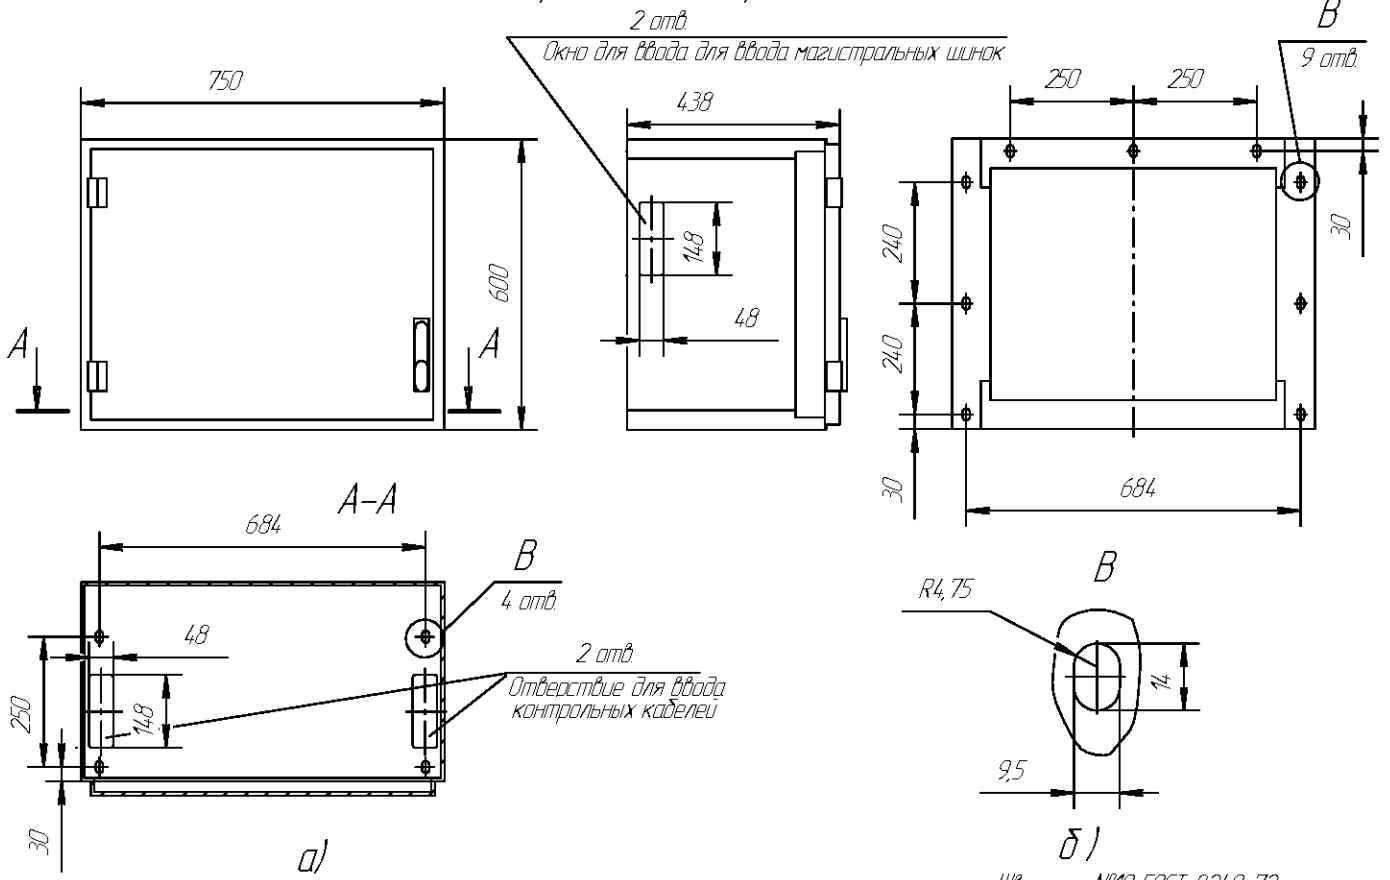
Габаритные, установочные, присоединительные размеры шкафов Шкаф типа ШВВ на номинальные токи 2000..4000 А с воздушным вводом, линейными и сборными шинами (транзит)
